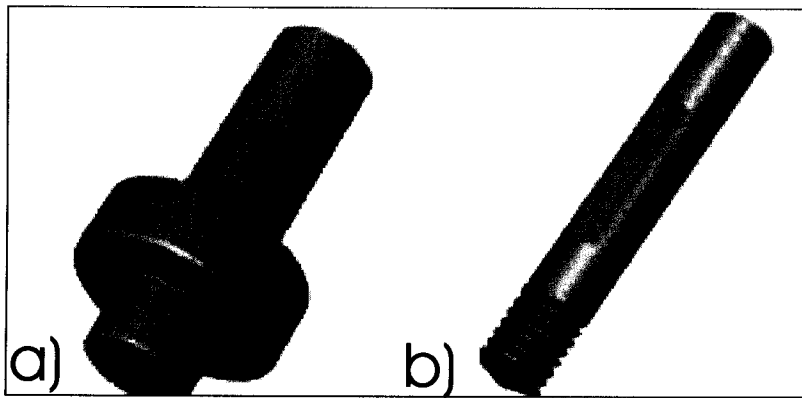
Shoulder em (a) e pino em (b), elementos que formam a ferramenta usada na *Friction Stir Welding*.
